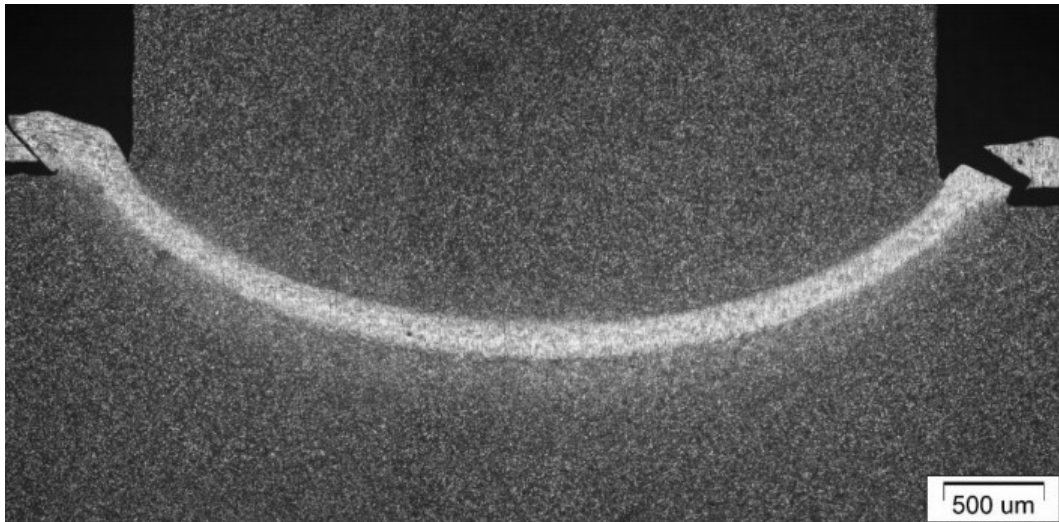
Пример макрошлифа образца с сечением сварного шва 6×26 мм
